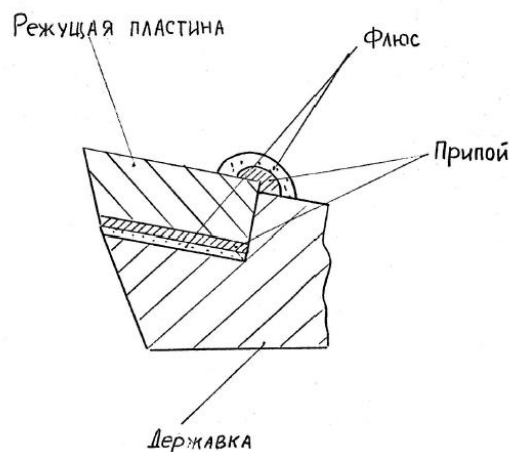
Кріплення ріжучої пластини припаюванням
